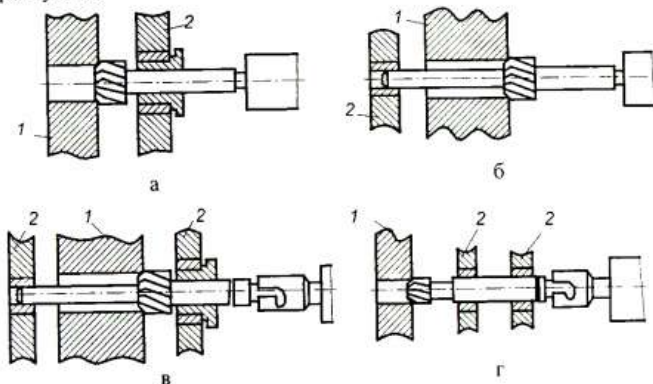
Принципові схеми направляючих елементів розточувальних кондукторів: а – передня направляюча, б – задня направляюча; в – передня і задня направляючі; г – подвійні передні направляючі; 1 – оброблювана деталь; 2 – кондуктор
